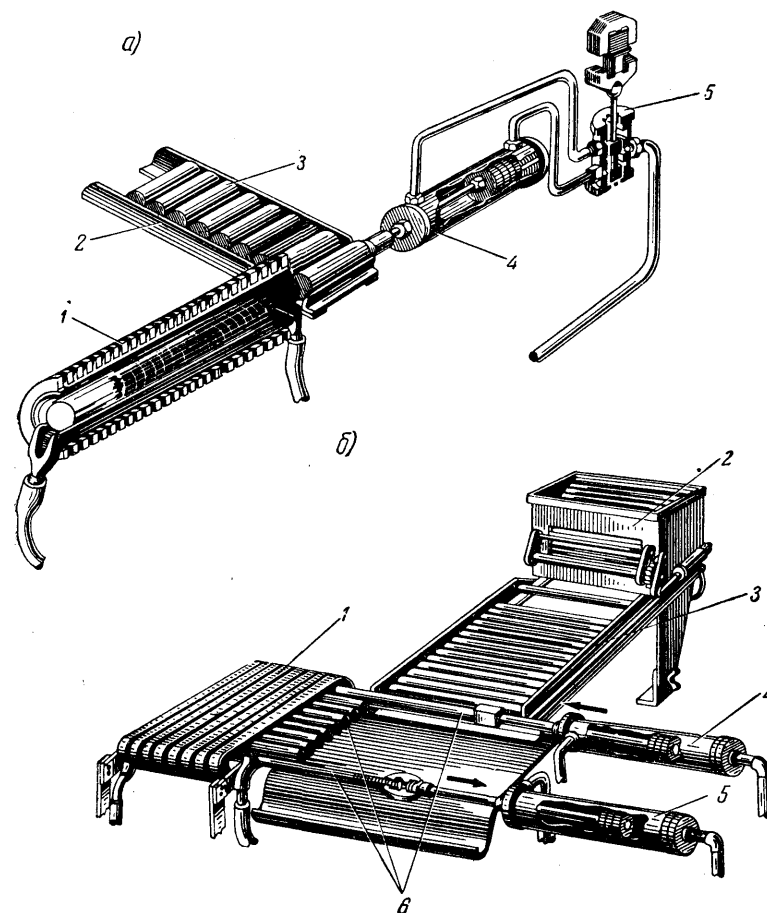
Кинематические схемы индукционных нагревательных установок непрерывного действия:
